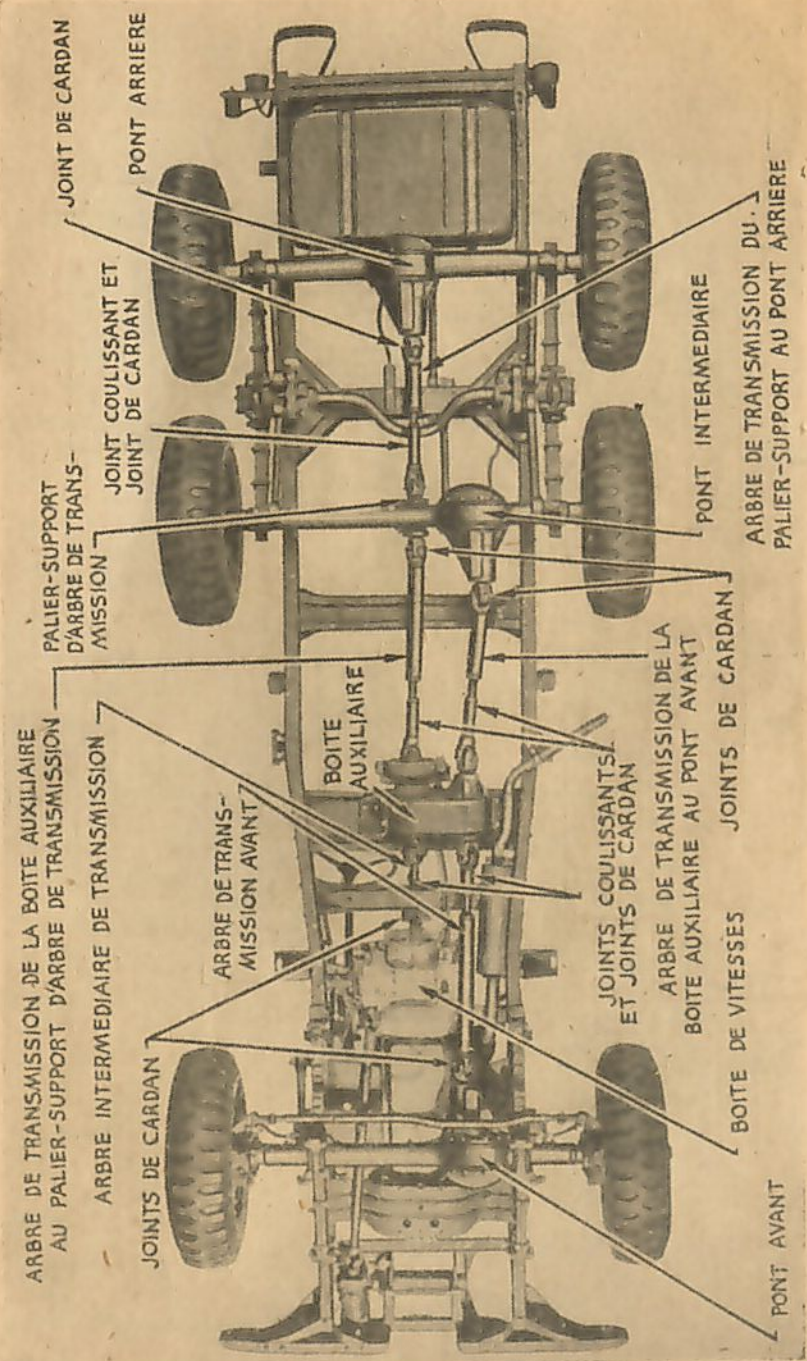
Vue par dessous du châssis 1 1/2 T. 6 x 6.
